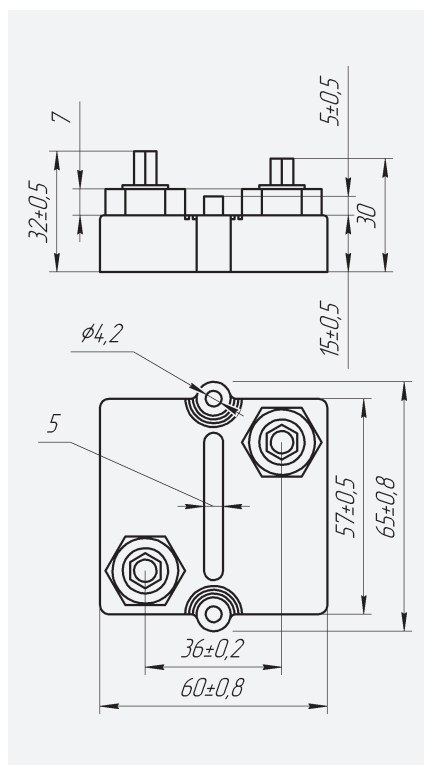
Габаритный чертеж резистора P1-150M 600 Вт и 800 Вт
